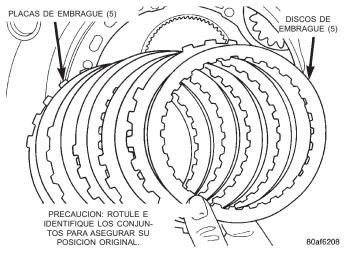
Instalación del conjunto de embrague de baja y marcha atrás
